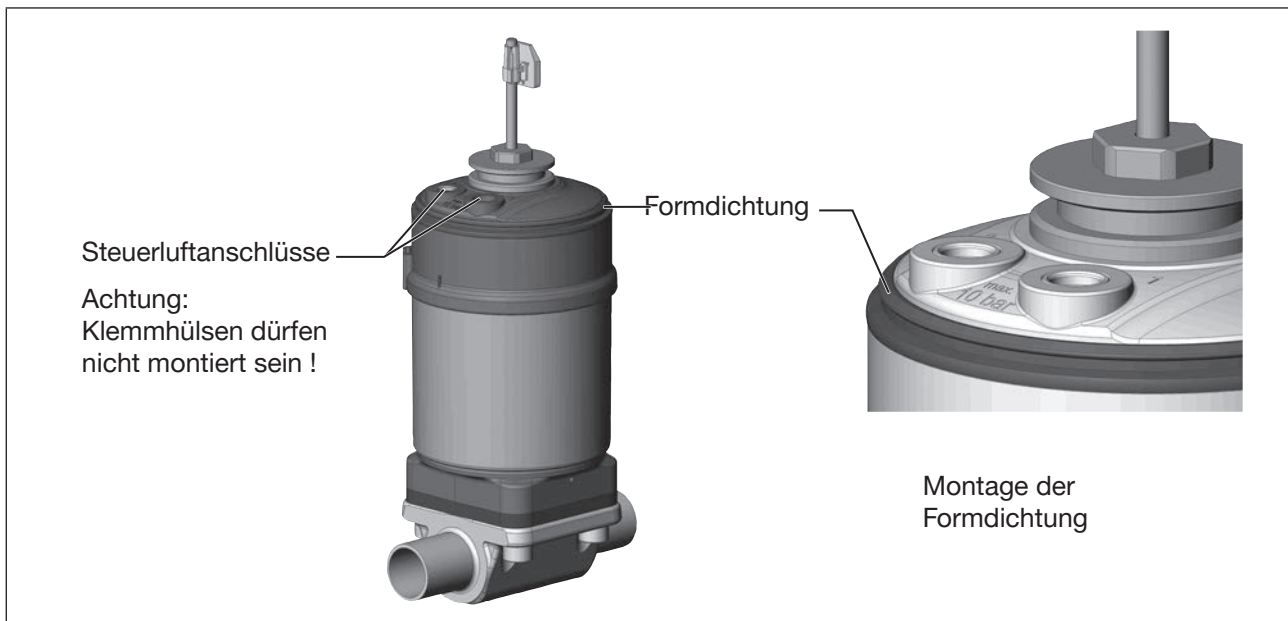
Montage der Dichtringe, Reihe 2103, 2300 und 2301
